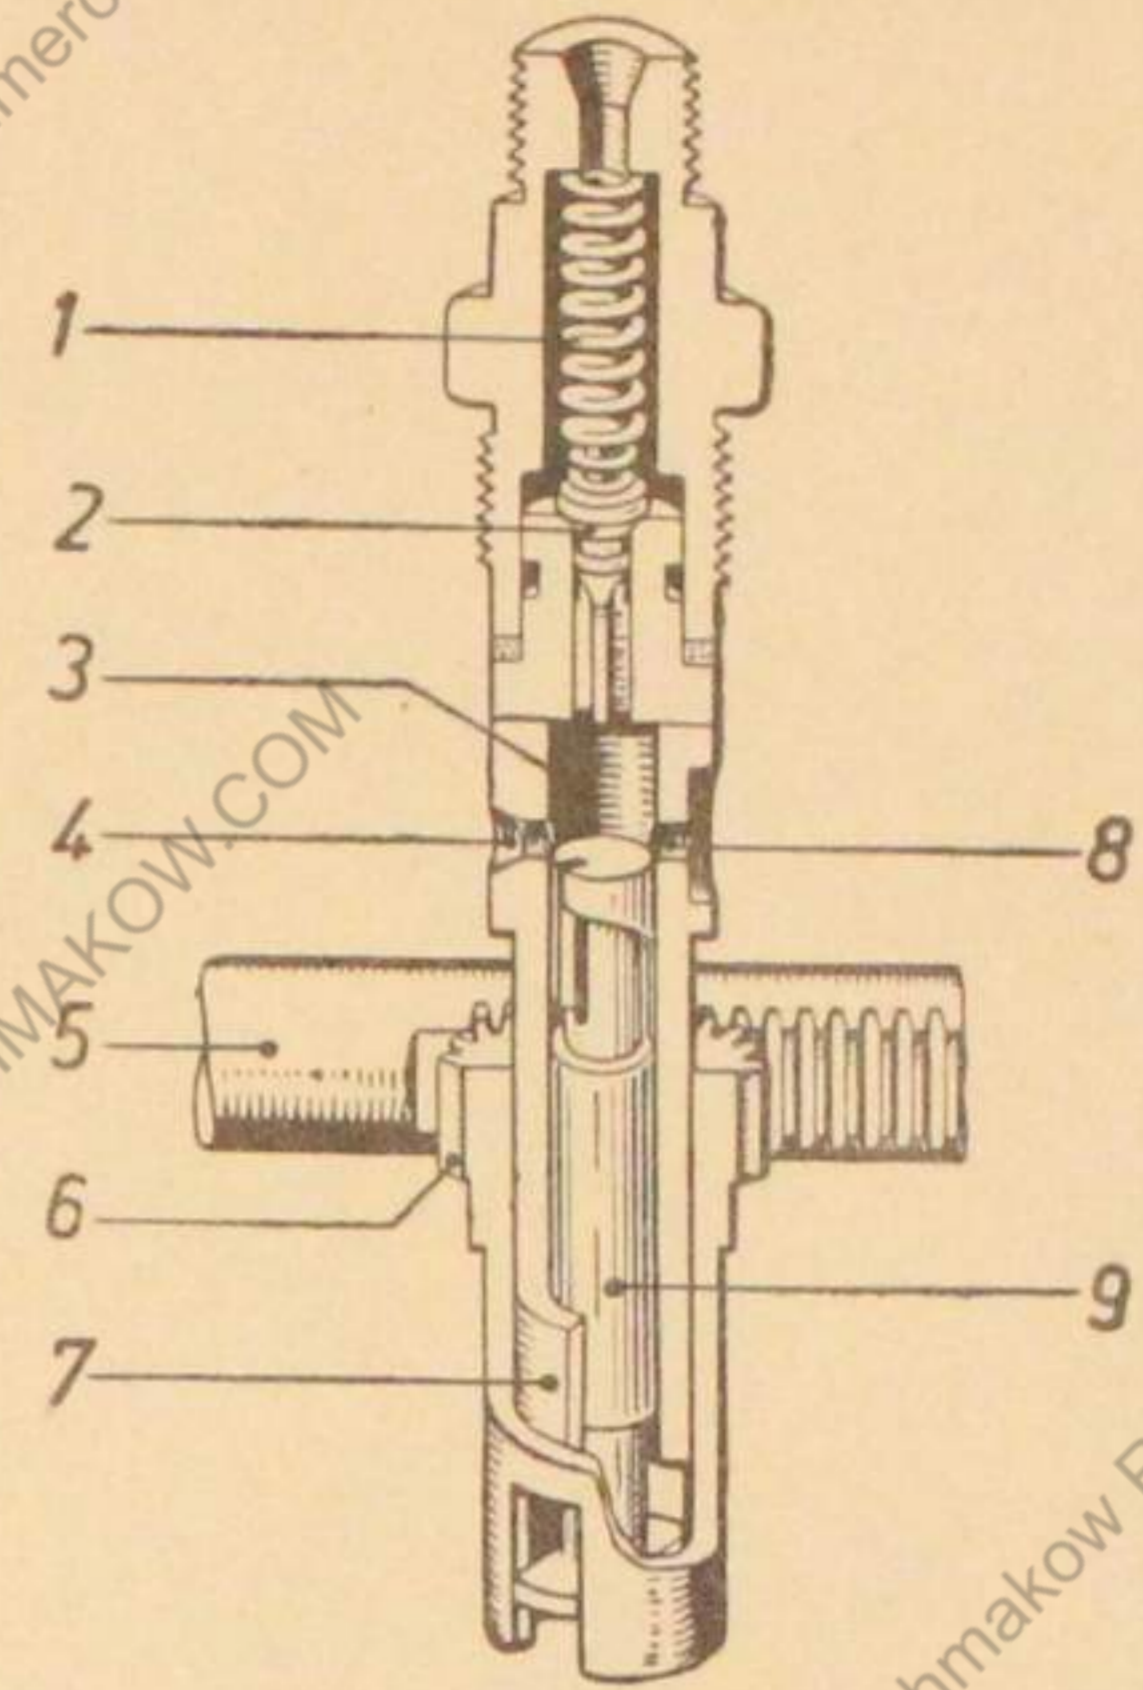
Pumpenelement der Bosch-Einspritzpumpe
